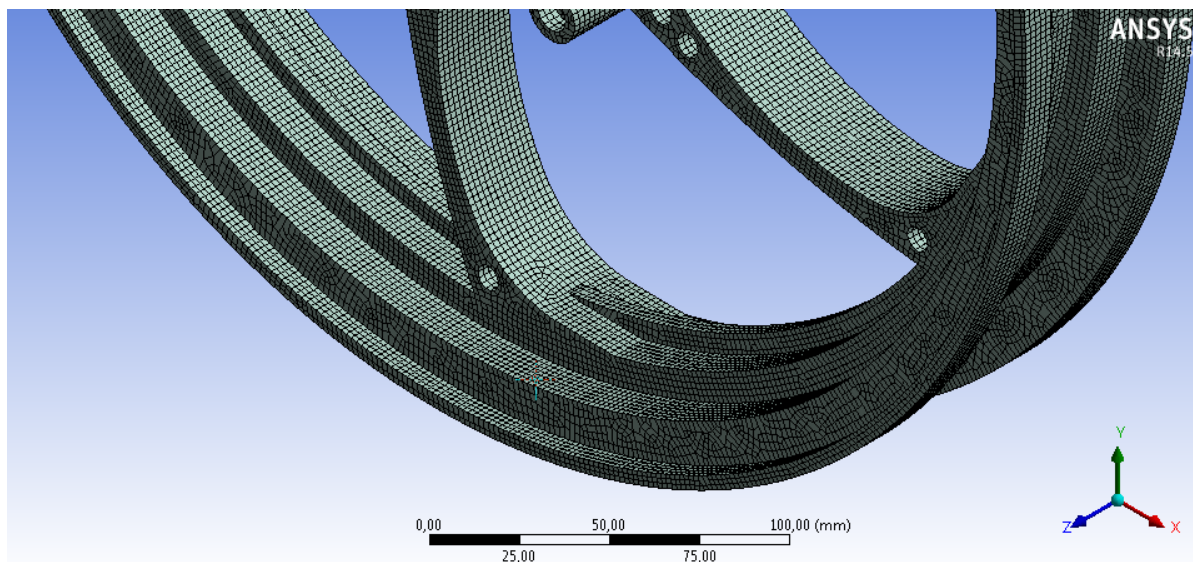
Mallado de elementos de 2 mm del diseño optimizado “a.4”. Fuente: Propia
